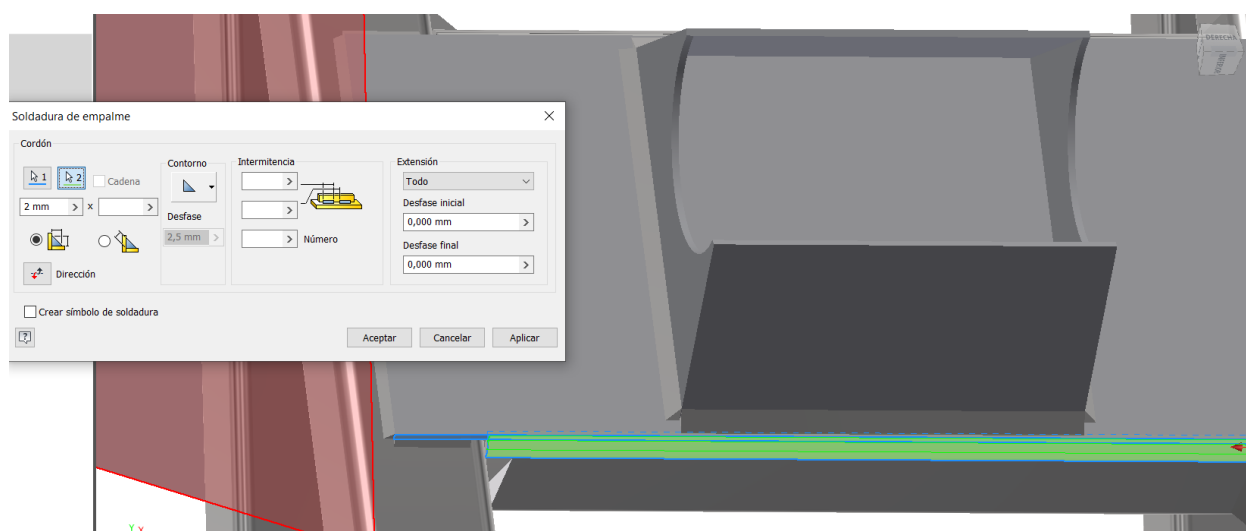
Soldadura de la placa de refuerzo de la base del eje basculante.
